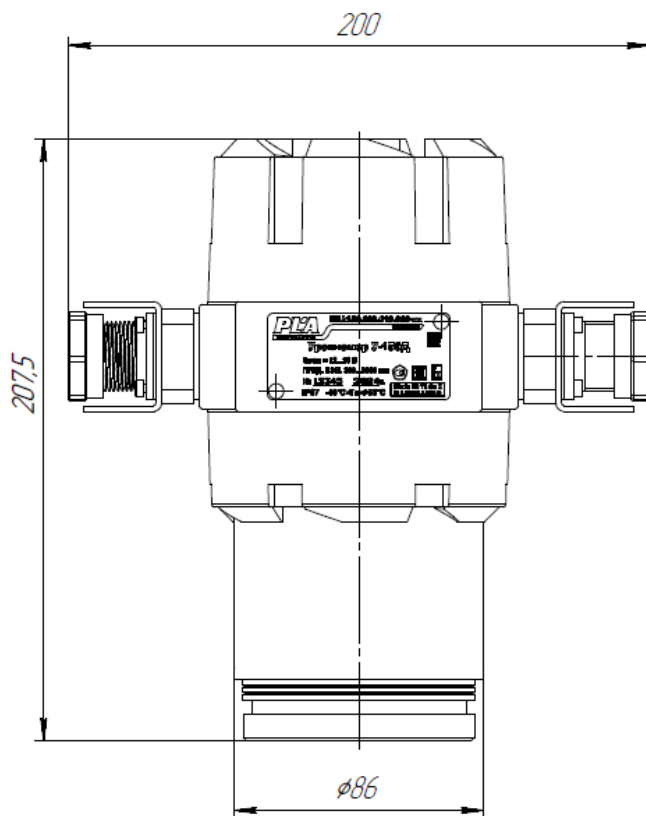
Габаритные и присоединительные размеры У-150Д
